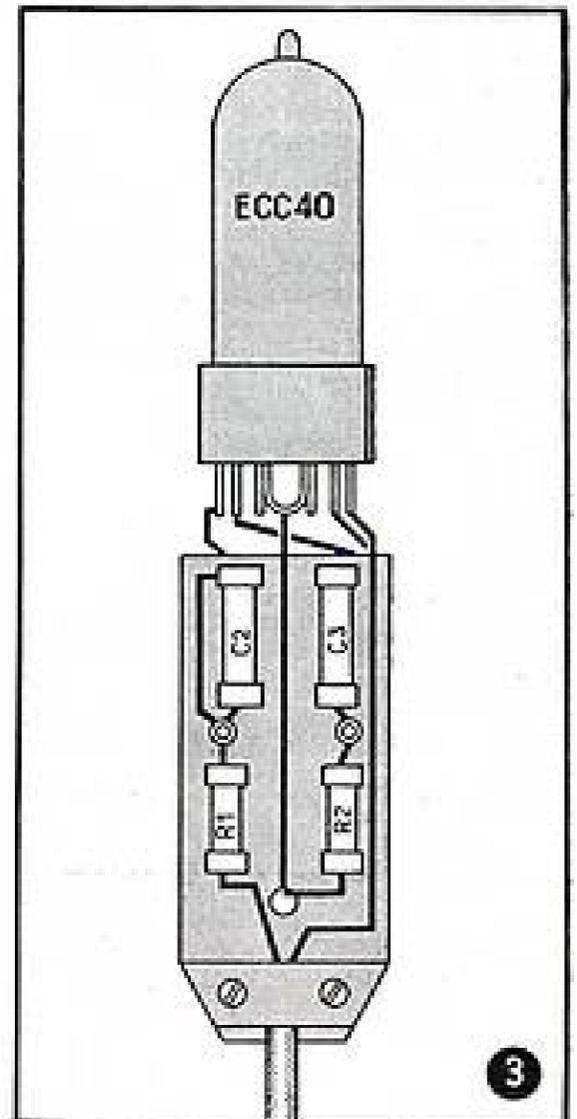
Disposition des pièces à l'intérieur du probe.
